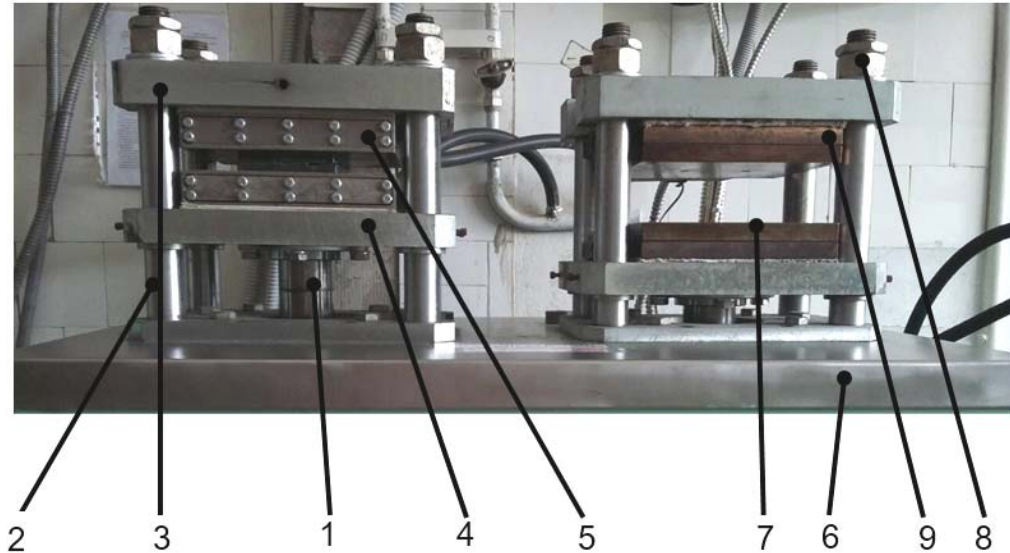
Багатоповерховий прес для виготовлення зубів:
